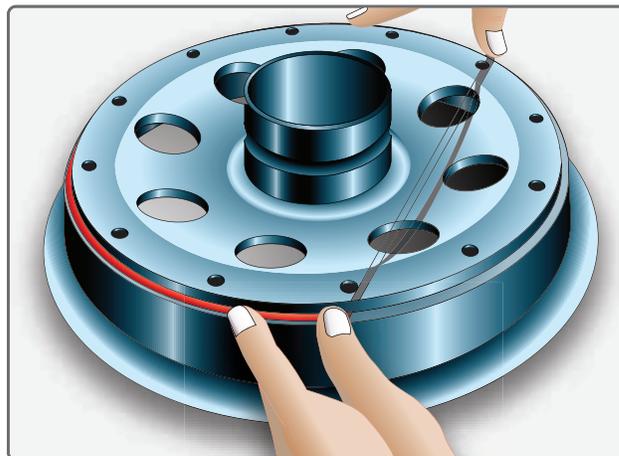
A meia roda de O-ring para uma roda de pneu sem câmara deve estar em boas condições e lubrificada para vedar por toda a vida útil do pneu. As superfícies de contato das metades da roda devem também estar em boas condições.
